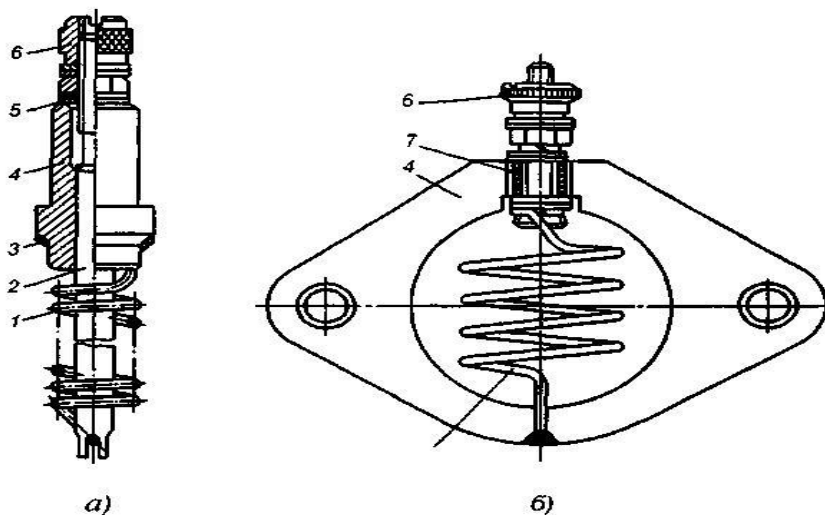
а - свеча подогрева воздуха во впускном коллекторе СН150; б - фланцевая свеча. 1 - спираль накаливания; 2 - стержень; 3 - уплотнительная шайба; 4 - корпус; 5 - изоляционная шайба; 6 - контактная гайка; 7 - изоляционная втулка
